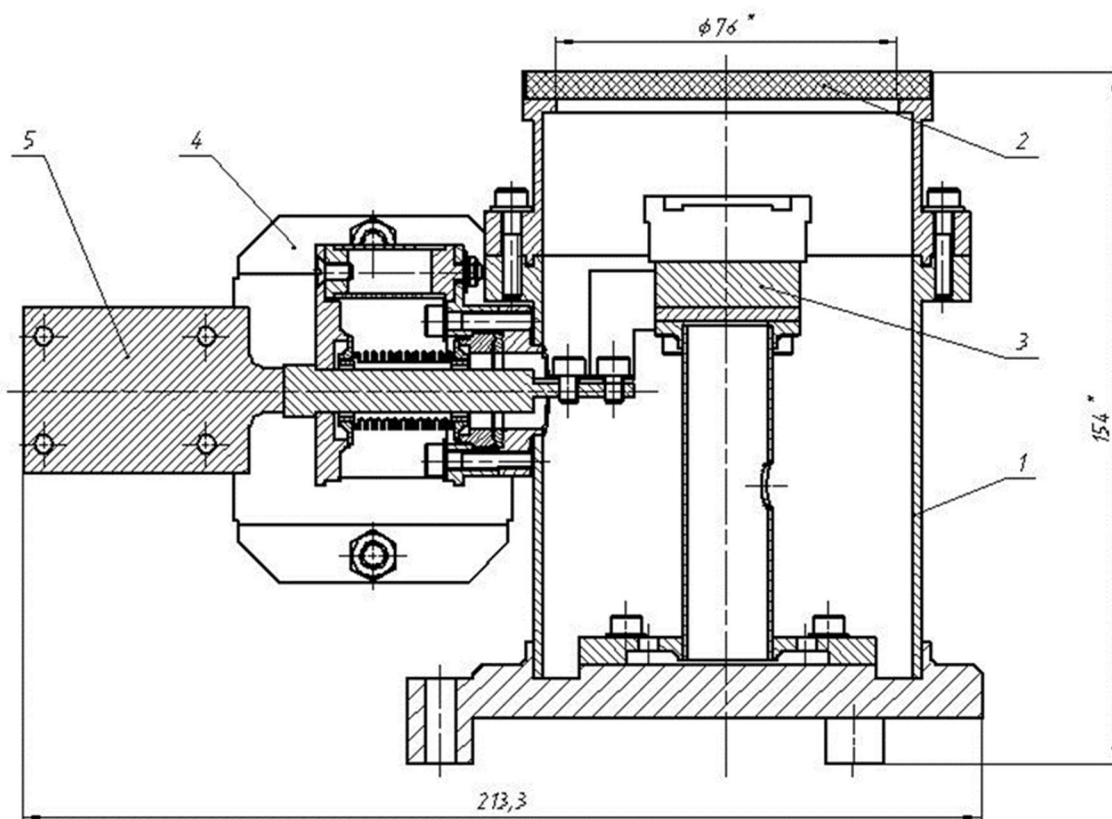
Чертеж общего вида БПИ. Здесь 1 – корпус БПИ, 2 – оконный блок, 3 – держатель ФПУ, 4 – магниторазрядный насос, 5 – хладопровод.
